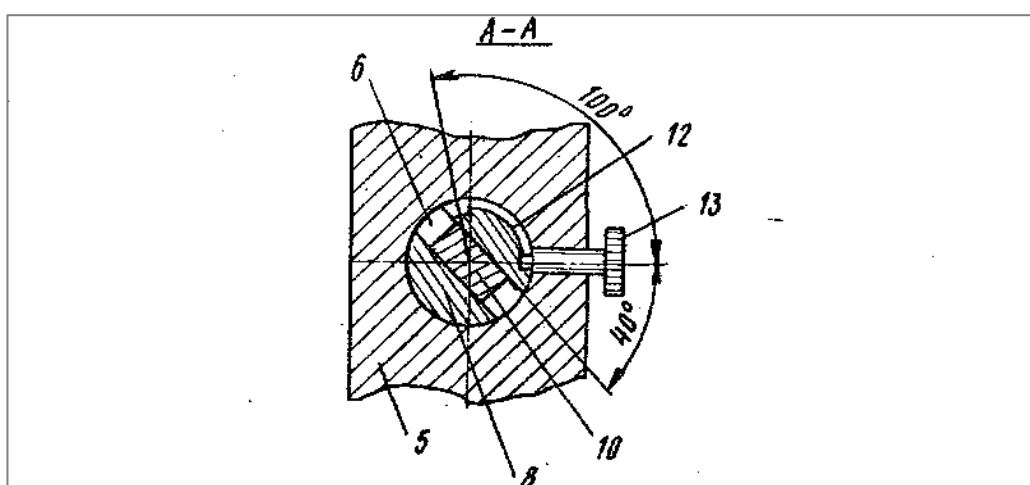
в – Устройство электроддержателя для сварки наклонным электродом
